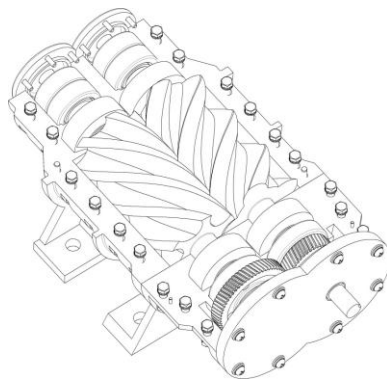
трехмерная модель компрессора со снятыми крышками.
